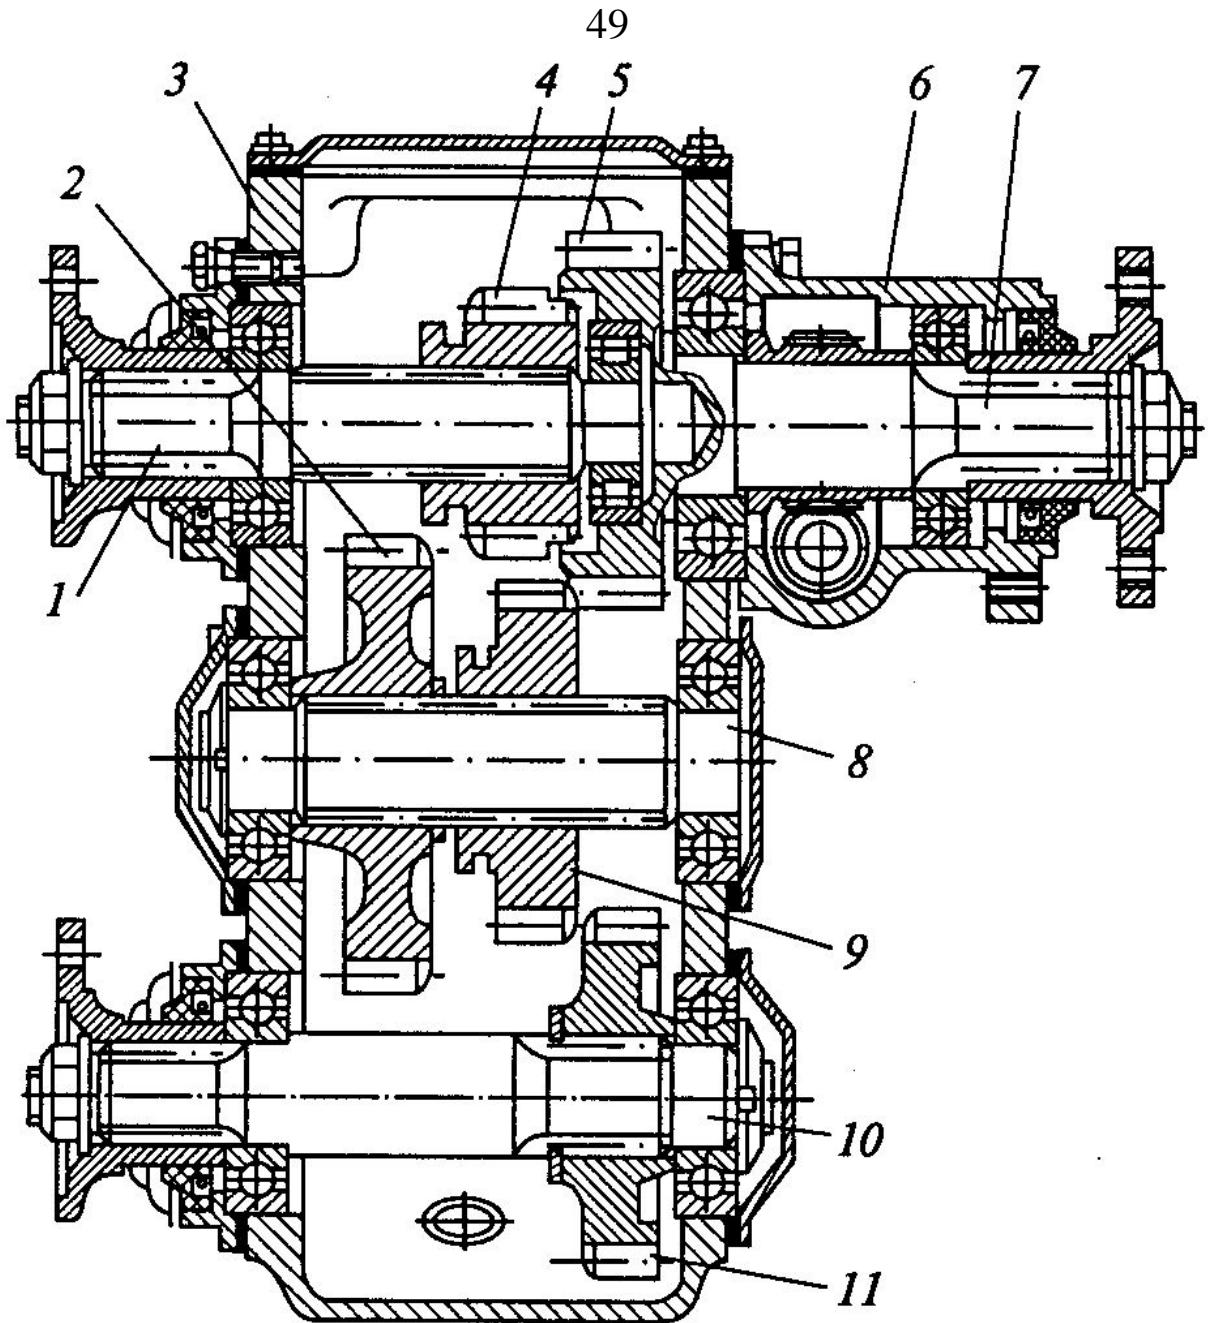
Раздаточная коробка автомобиля ГАЗ-66
